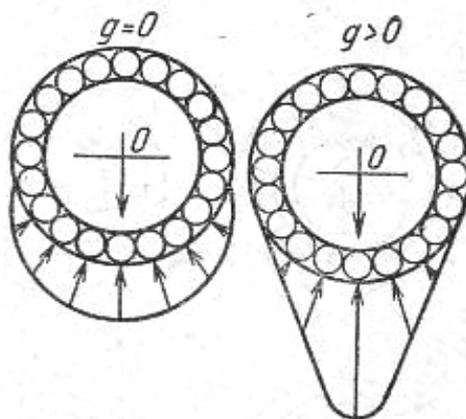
Фронтальная схема нагружения колец подшипника: g - рабочий зазор между телами качения и роликами
